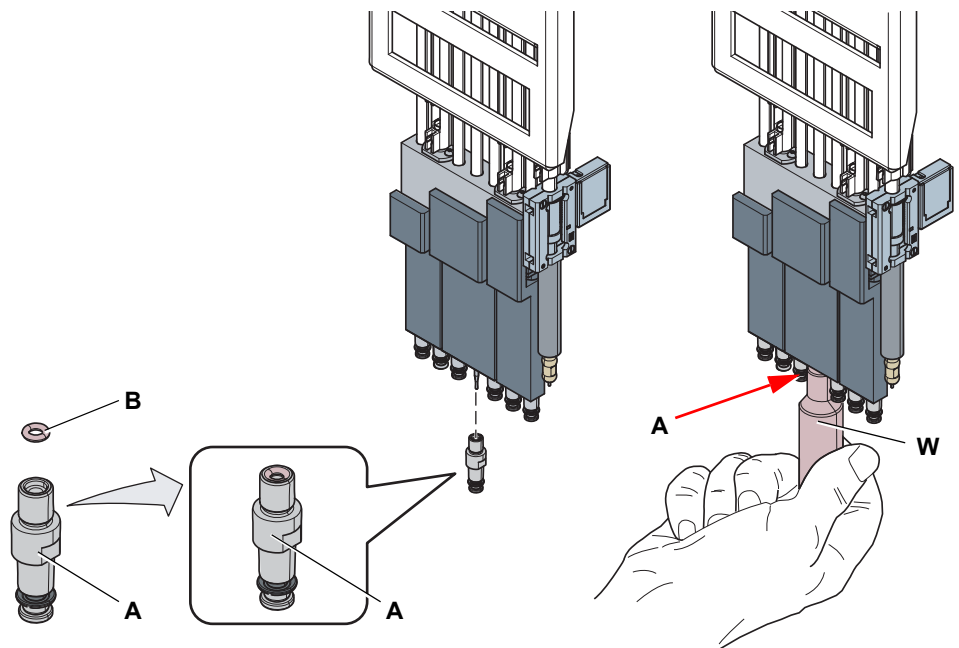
Matrice à 7 embouts, installation du cône pour DiTi
